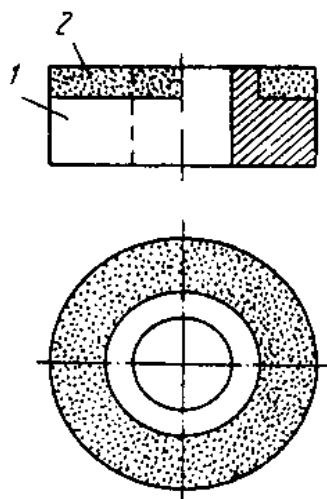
Різець циліндричний поворотний з напайним твердосплавним диском (1 – державка різця; 2 – твердосплавний диск)
